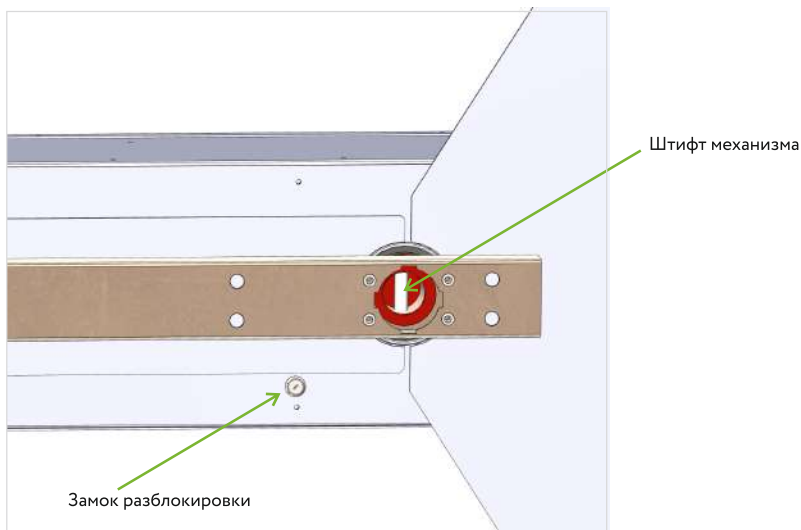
Место установки верхнего подшипникового узла (вид снизу)
